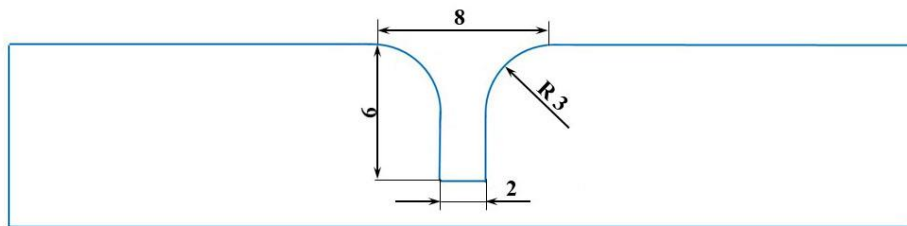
Ескіз форми формуючої канавки в сталевій підкладці, призначеній для плазмо-дугового зварювання алюмінієвих сплавів товщиною 6 – 8 мм.
